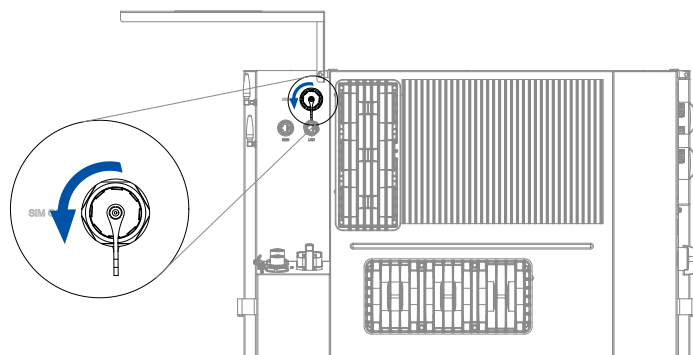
Desserrage du couvercle du logement pour carte SIM
